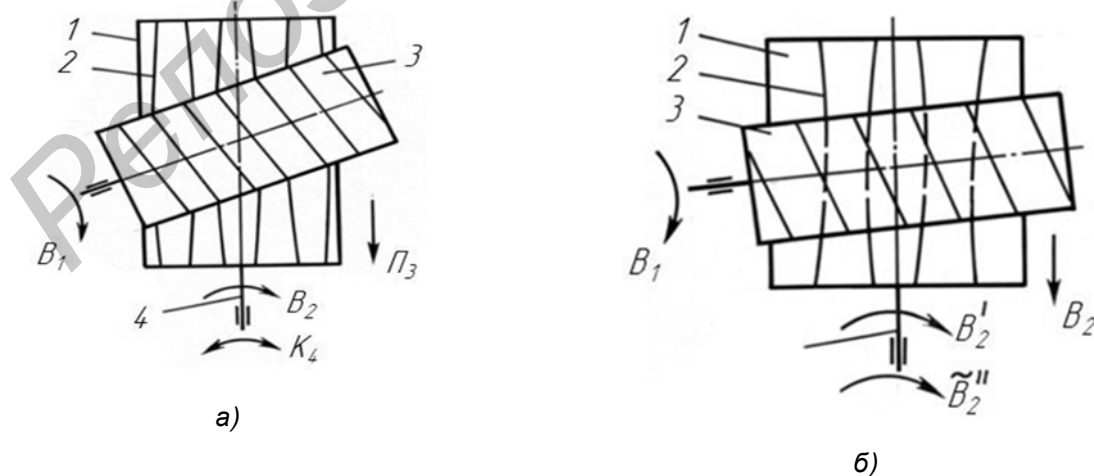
Схемы обработки зубчатых колес с бочкообразными зубьями при совмещении исполнительных движений: а — схема с совмещенными вращательным и возвратно-вращательными движениями; б — схема с двумя совмещенными вращательными движениями
